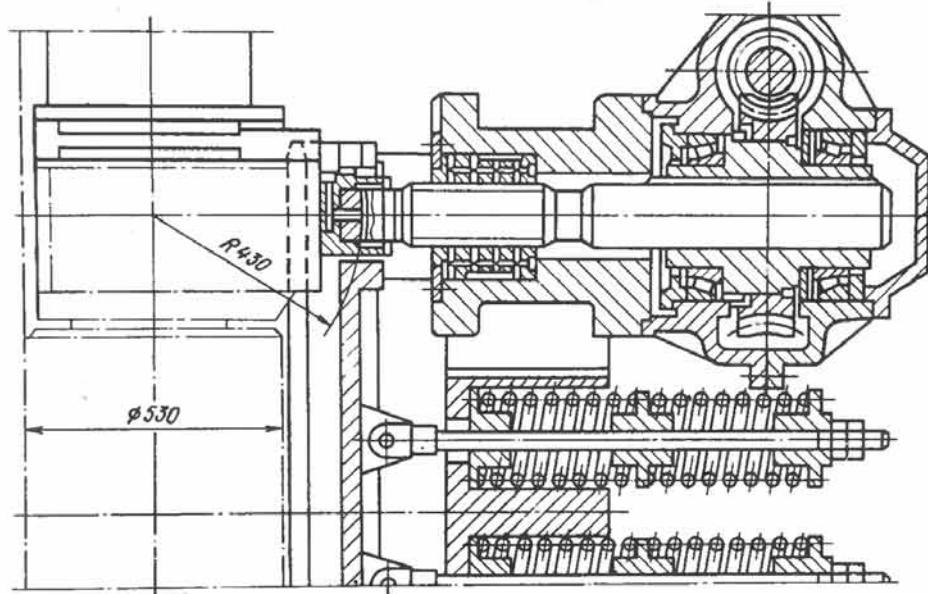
Пружинное уравновешивание верхнего вала клети 530 непрерывного заготовочного стана 700/500
